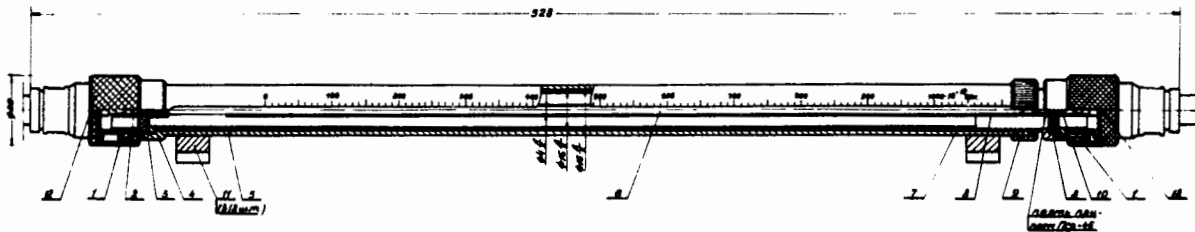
Общий конструктивный (сборочный) чертеж переменной линии задержки.
